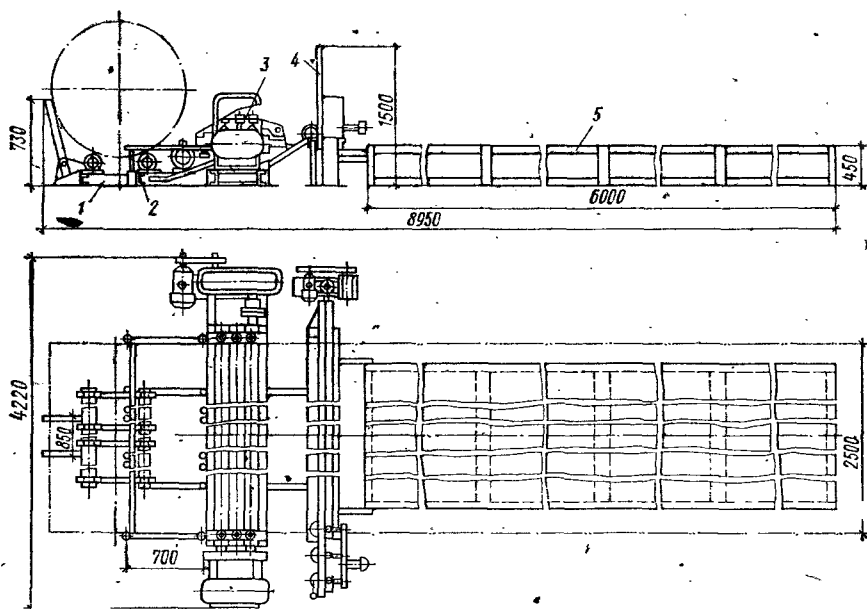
Установка конструкции ЦНИИОМТП для правки и резки рулонных сеток:
